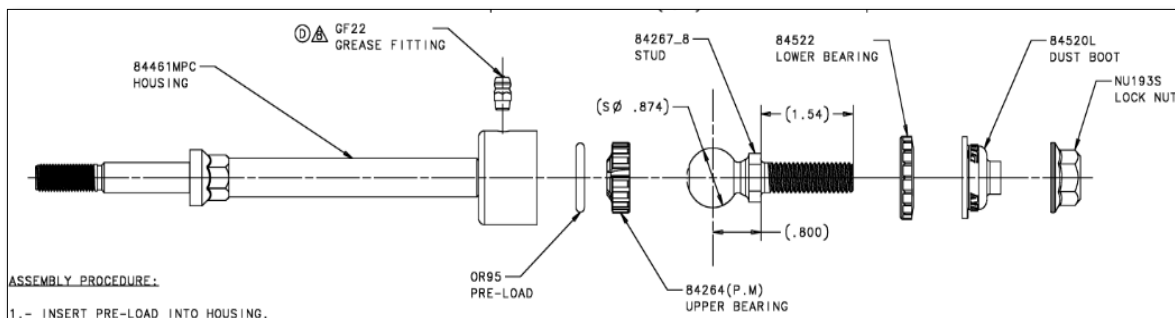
Plano del ensamble AMGK80894 con la explosión de componentes necesarios para su fabricación.
